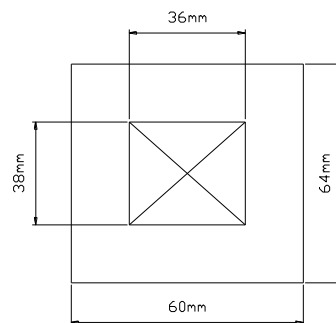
Dimensiones de la tapa del Carrete
